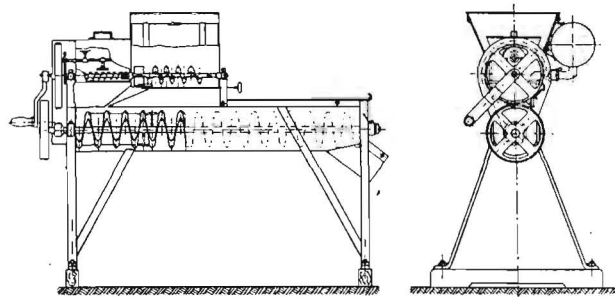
Schema des Universal-Samenbeizgerätes PU-1,0
